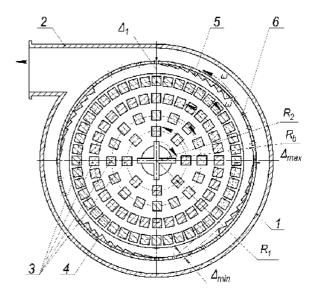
Схема камеры помола дезинтегратора с цилиндрическим калибрующим устройством: 1 — корпус; 2 — разгрузочный патрубок; 3 — ударные элементы; 4 — цилиндрическое калибрующее устройство; 5 — бронеплиты; 6 — перфорированная секция
